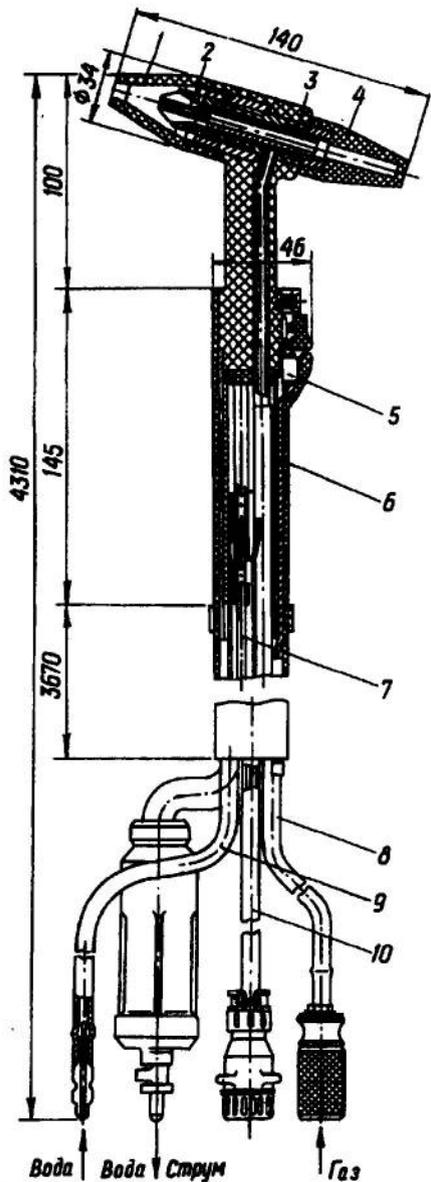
Пальники для ручного зварювання типу ГР:
